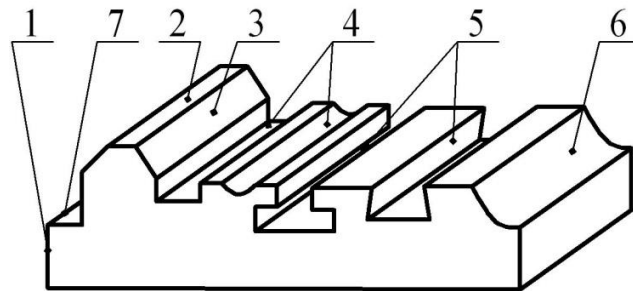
Типові поверхні, одержувані при струганні
